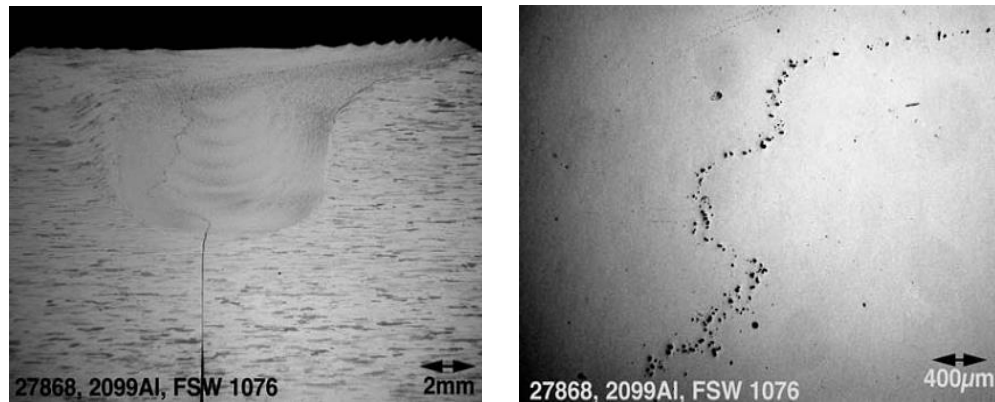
a) Micrografía mostrando un defecto de línea remanente, en soldadura FSW y b) Residuos de óxido presentes en la superficie de las piezas de trabajo a unir Leonard et al. (2003).
